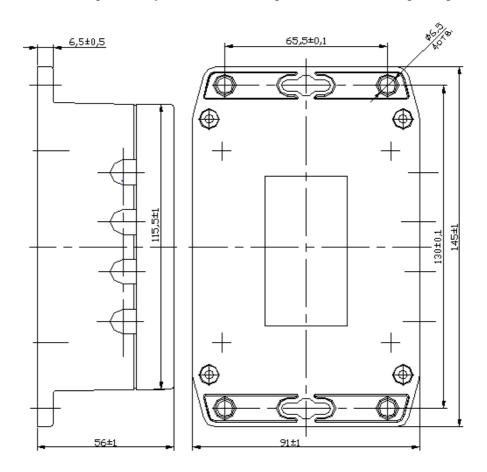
Габаритные, установочные и присоединительные размеры БВВ.01
